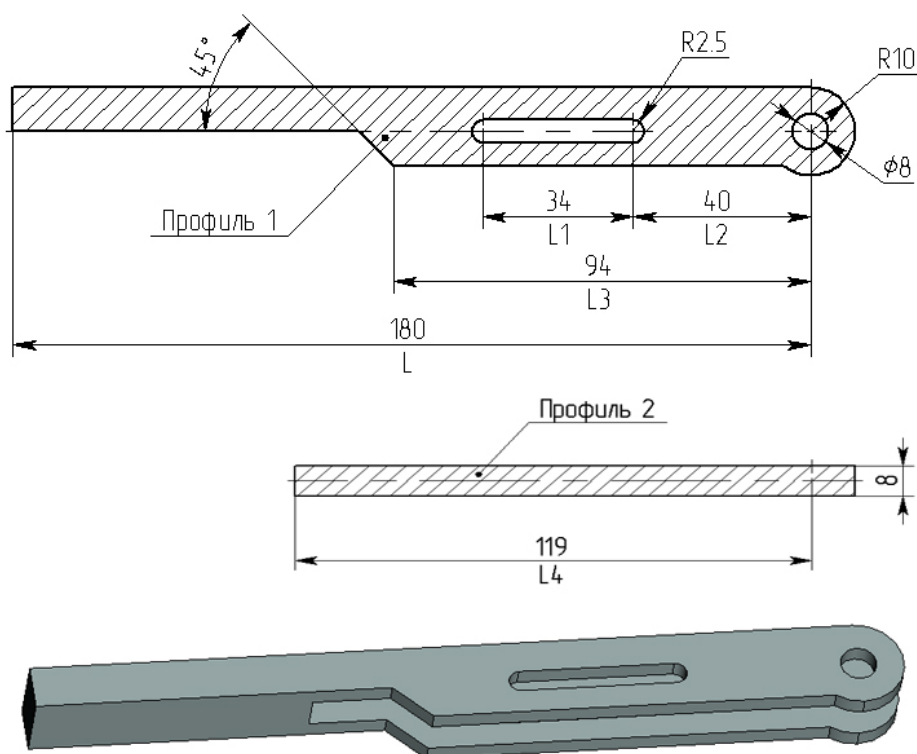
Чертеж и 3D модель детали «Рычаг»
